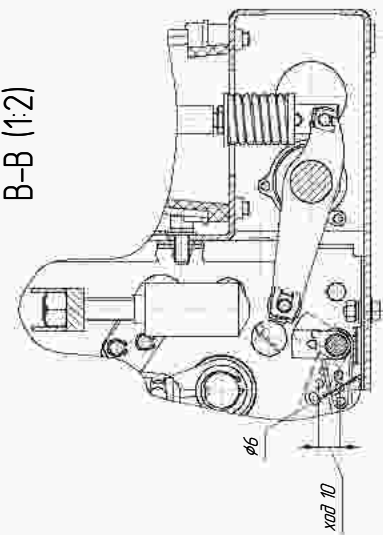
Габаритные, присоединительные и установочные размеры выключателя типа ВВУ-СЭЩ-ПЗ-10-20(31,5)/
